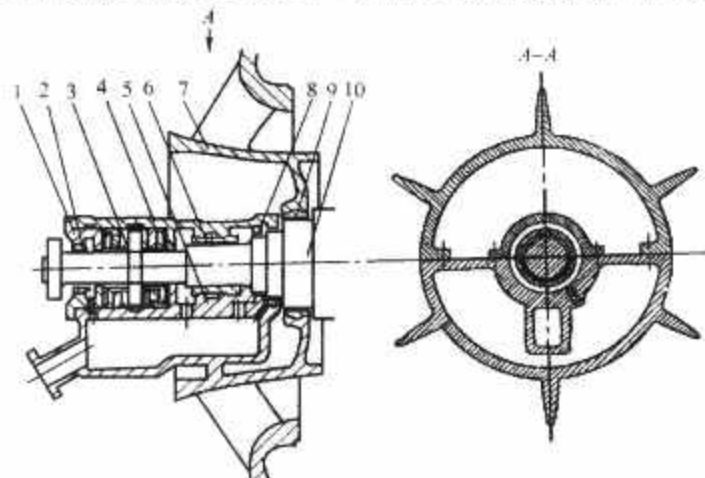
轴承座下半与进气机匣铸成整体的结构
